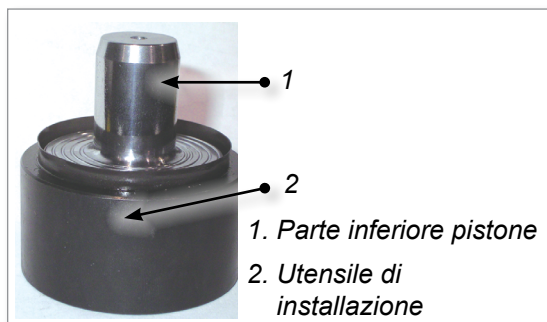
Parte inferiore del pistone con utensile di installazione
